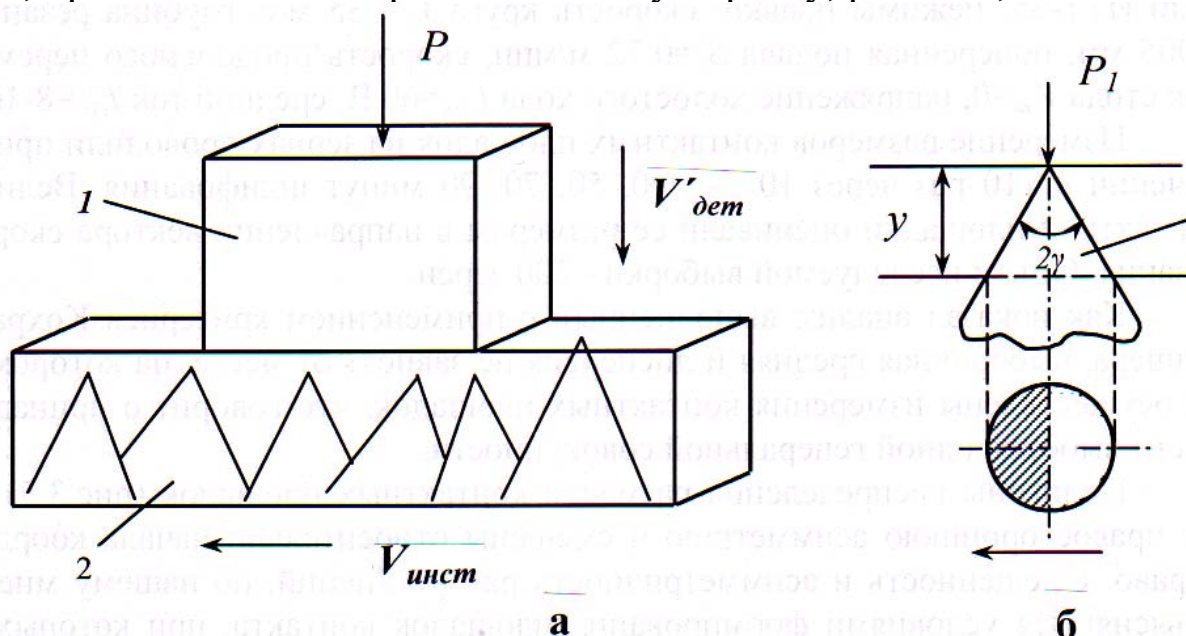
Расчетная схема: 1 – обрабатываемая деталь; 2 – абразивный инструмент; 3 – режущее зерно.
